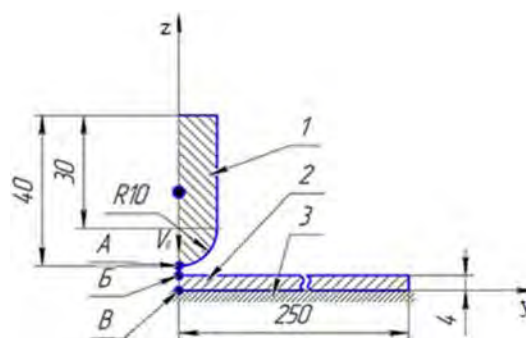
Розрахункова схема процесу динамічного навантаження пластини, що динамічно обробляється: 1 – індентор; 2 – пластинка; 3 – абсолютно жорстка опора, А – точка на зовнішній поверхні індентора, В – точка на зовнішній поверхні пластини, В – точка на тильній поверхні пластини
